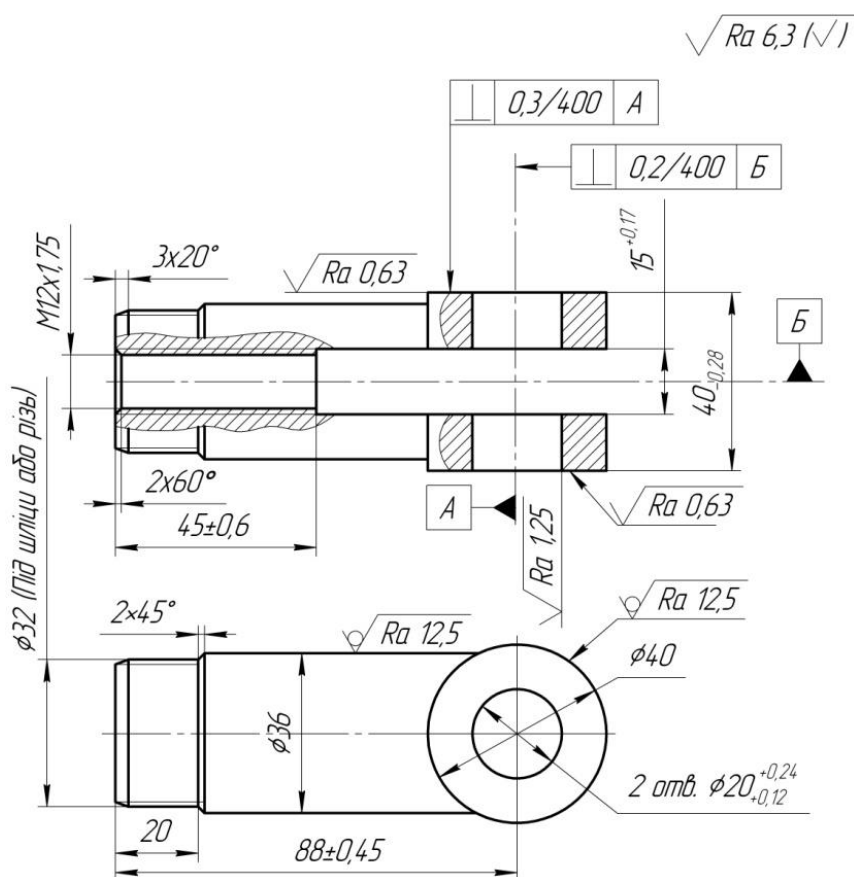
Креслення деталі «Вилка тяги»
